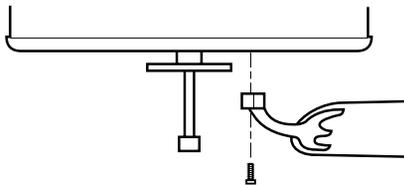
Forma de instalar los soportes de hierro al conjunto del ventilador.
